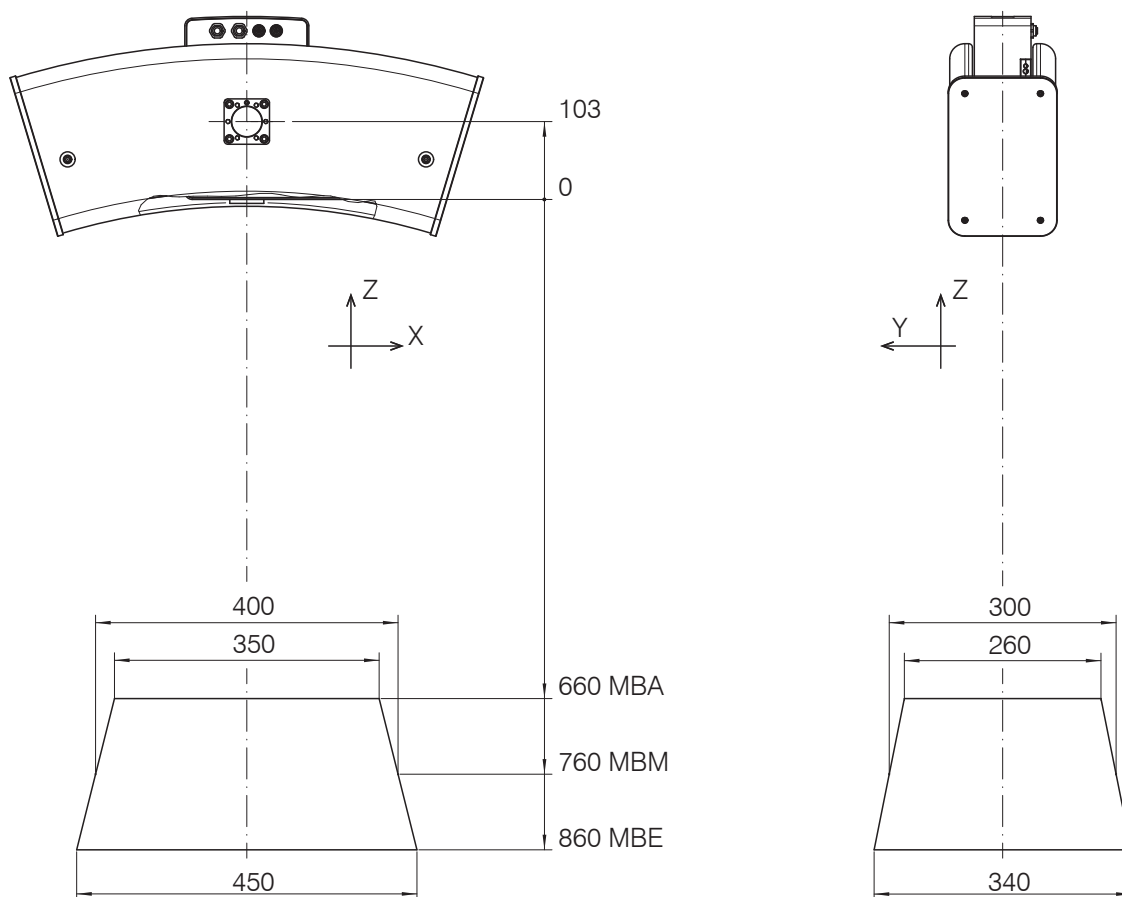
Maßzeichnung Messfeld surfaceCONTROL 3D SC25x0-400
